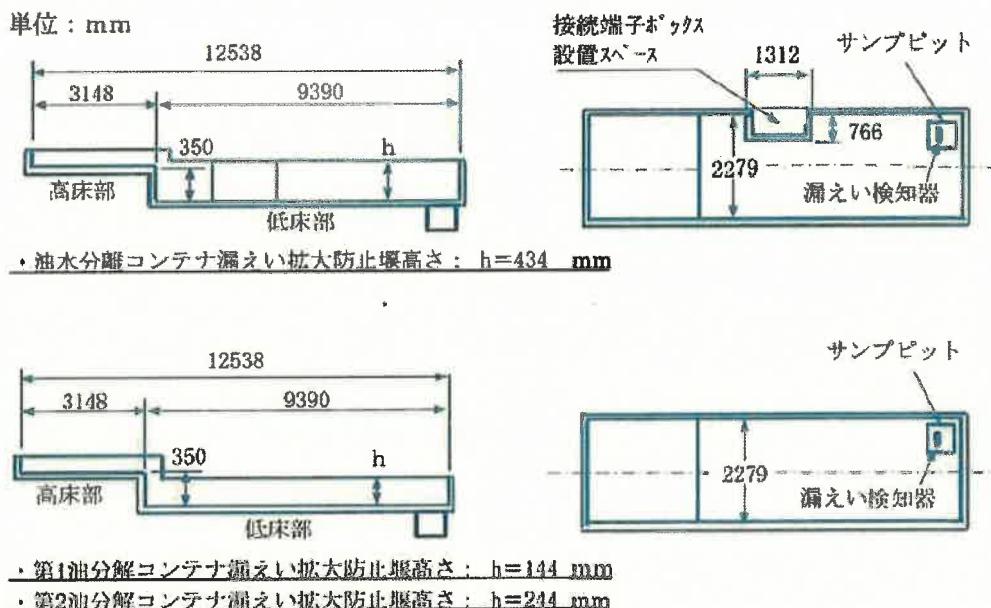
漏えい拡大防止堰の寸法 (単位: mm)
